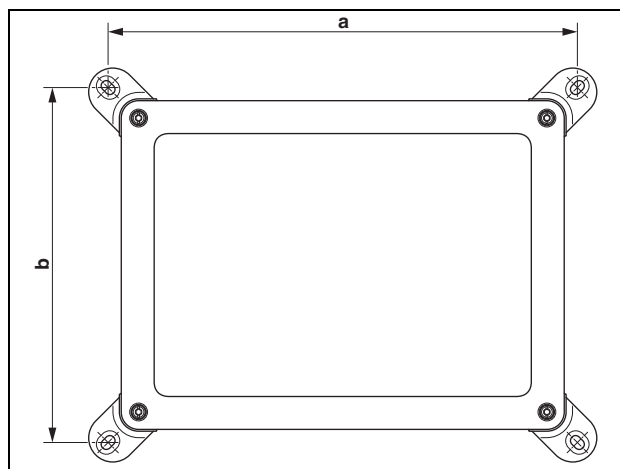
Wandhalterung UCS WM-B..., Bohrplan
